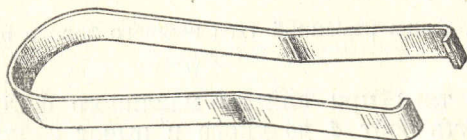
Щипцы для вынимания кулачковой шайбы.
